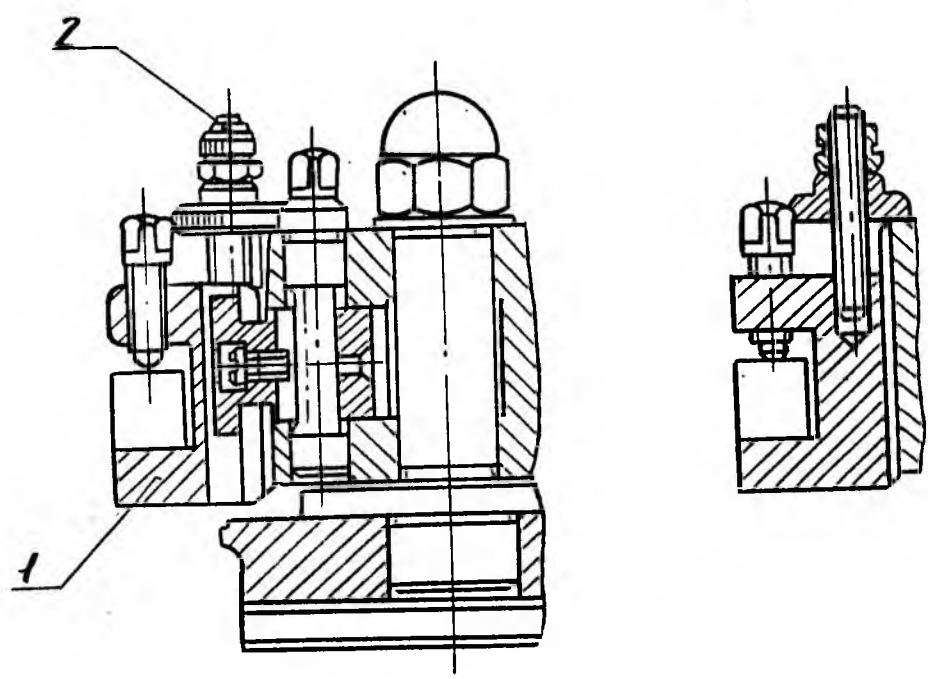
Двухпозиционный непереворотный резцедержатель с быстросменными блоками.
